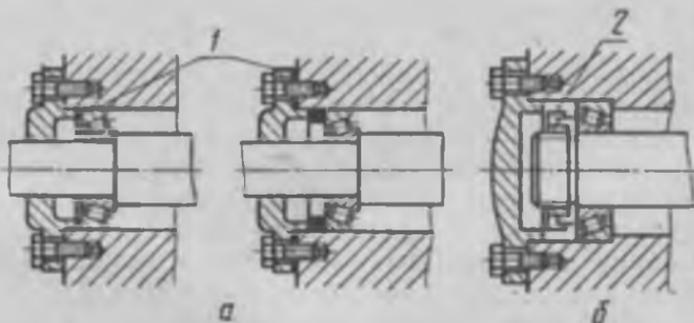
Регулировка зазора у конических и роликовых подшипников:
